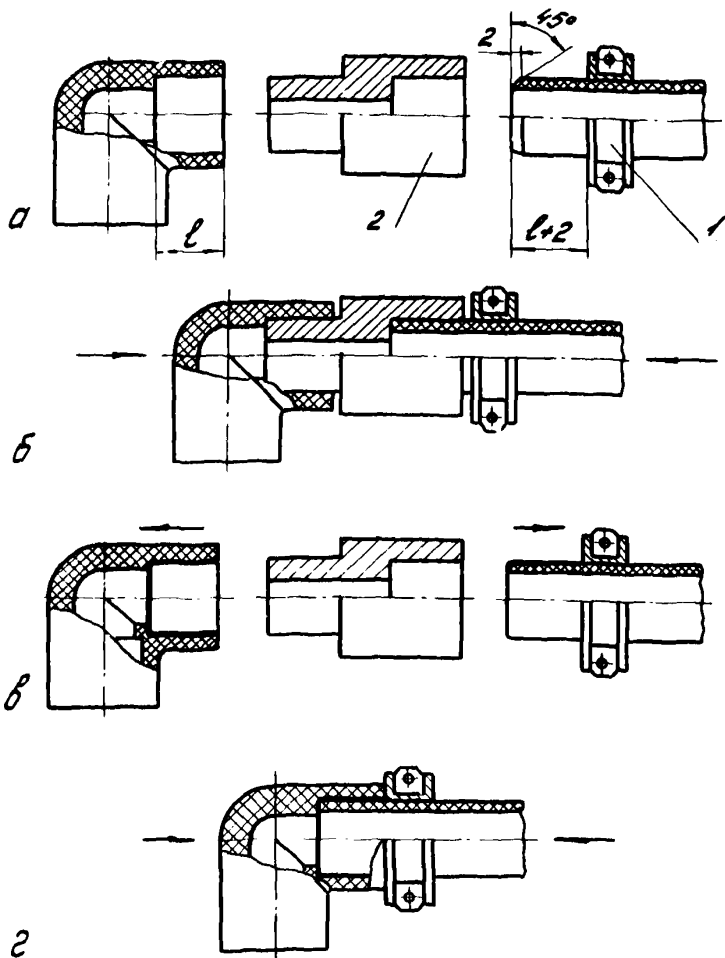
Последовательность процесса контактной сварки в раструб труб и соединительных деталей из ПВД:
